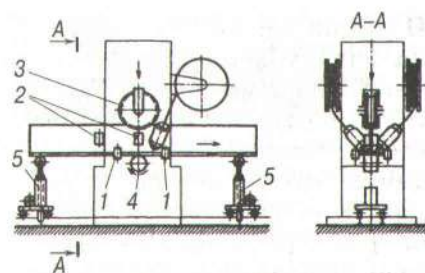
Схема верстата для зварювання балок таврового профілю:
